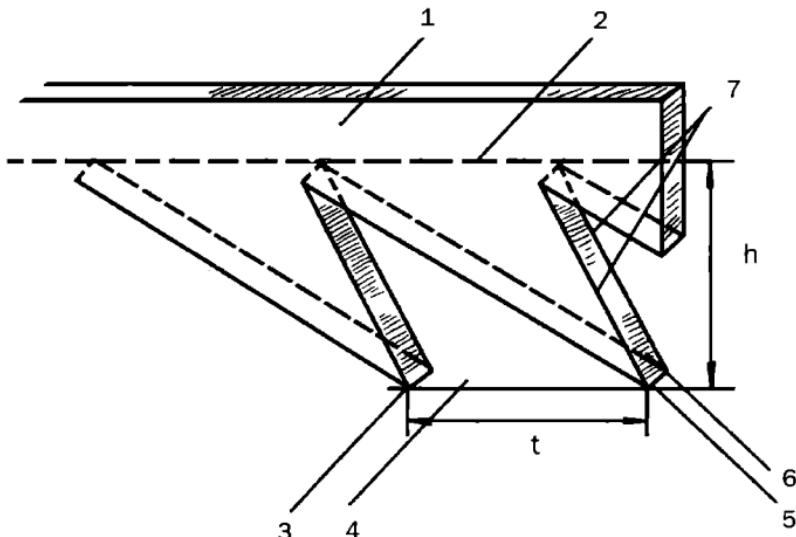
Элементы пилы (h — высота зуба; t — расстояние между смежными зубьями): 1 — полотно; 2 — линия основания зубьев; 3 — вершина зуба; 4 — пазуха; 5 — передняя кромка; 6 — передняя грань; 7 — боковые режущие кромки
